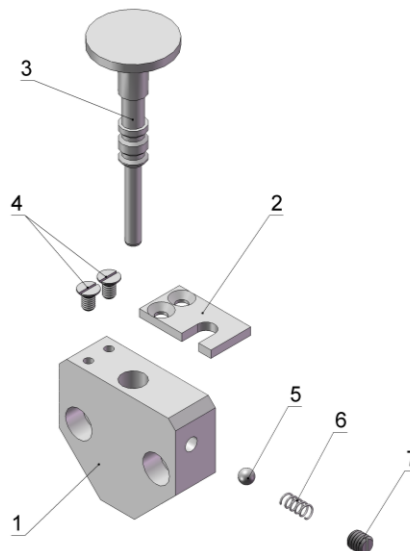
Механизм замыкателя автоподачи отрезного суппорта в сборе
